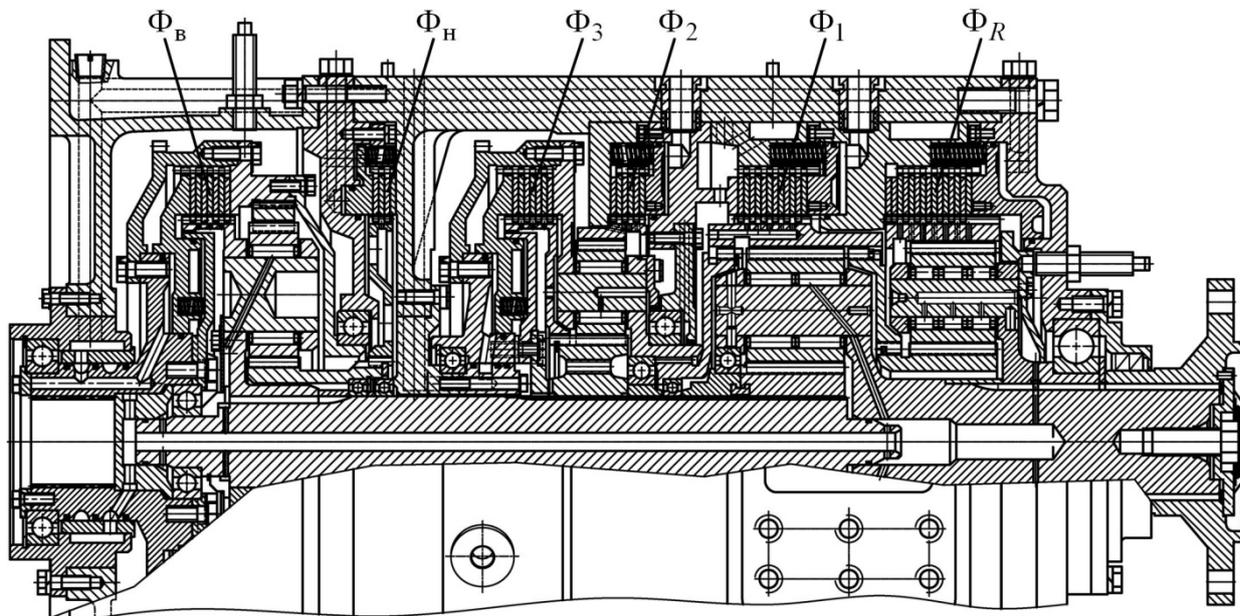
Конструкция ПКП гидромеханической передачи карьерного самосвала БелАЗ–75570
